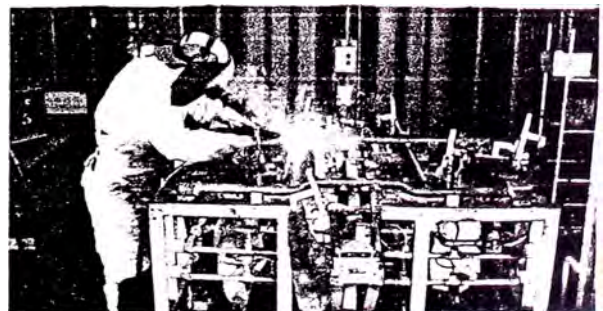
Proceso de soldadura uso dispositivos de soldadura chasis
